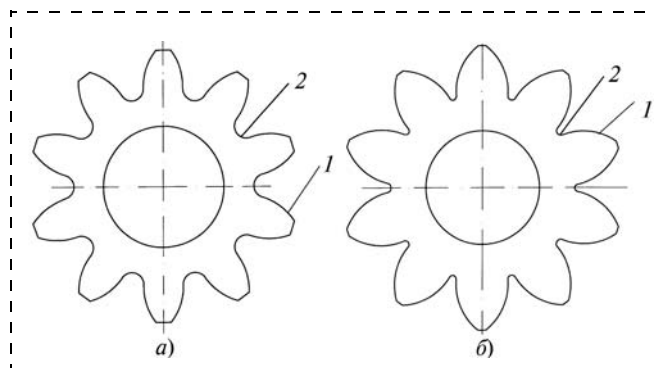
Профили зубьев звезды при тангенциальном смещении профилей (а) и без смещения (б): 1 — боковая, рабочая поверхность зуба; 2 — галтель зуба
